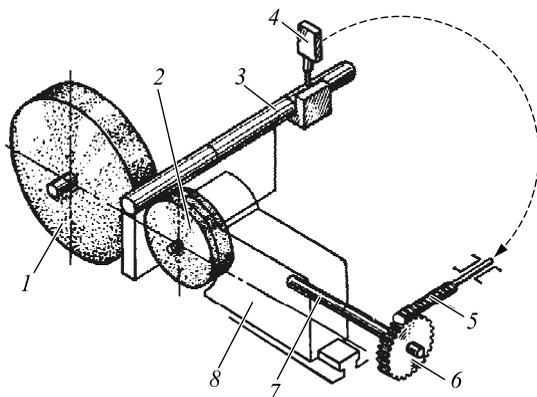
Схема подналадчика к бесцентрово-шлифовальному станку
